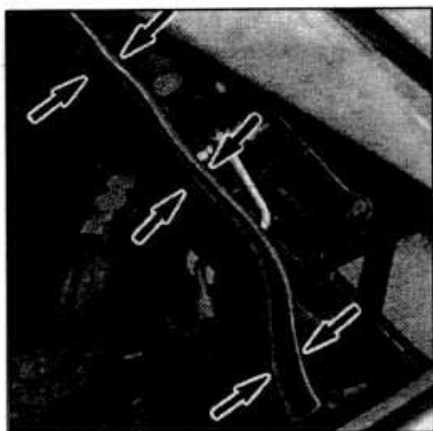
Проверка положения уплотнителя верхней кромки щита передка
